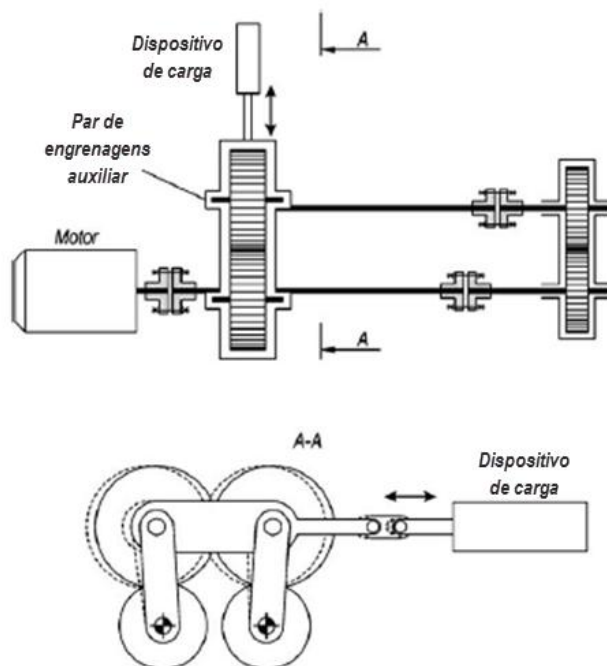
Torque aplicado por movimentação de par de engrenagem auxiliar (HARALD e LÖHR,1980)
